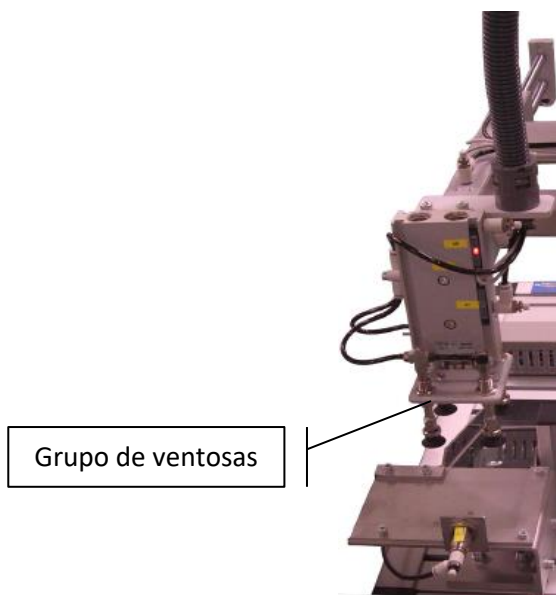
Manipulador. Fuente: (www.smc.eu)
